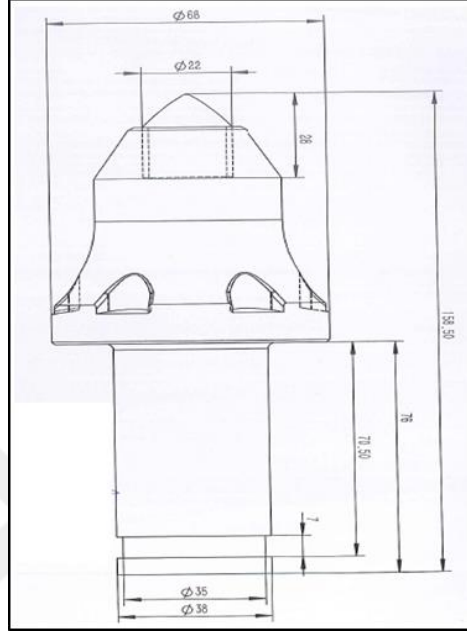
DH R75T Technong keski teknik çizimi.
